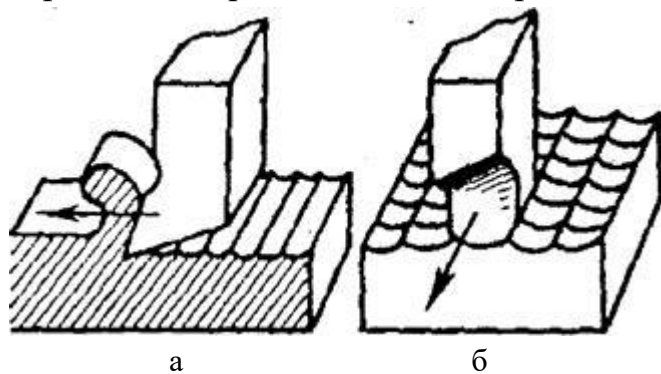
Продольная (а) и поперечная (б) шероховатость
